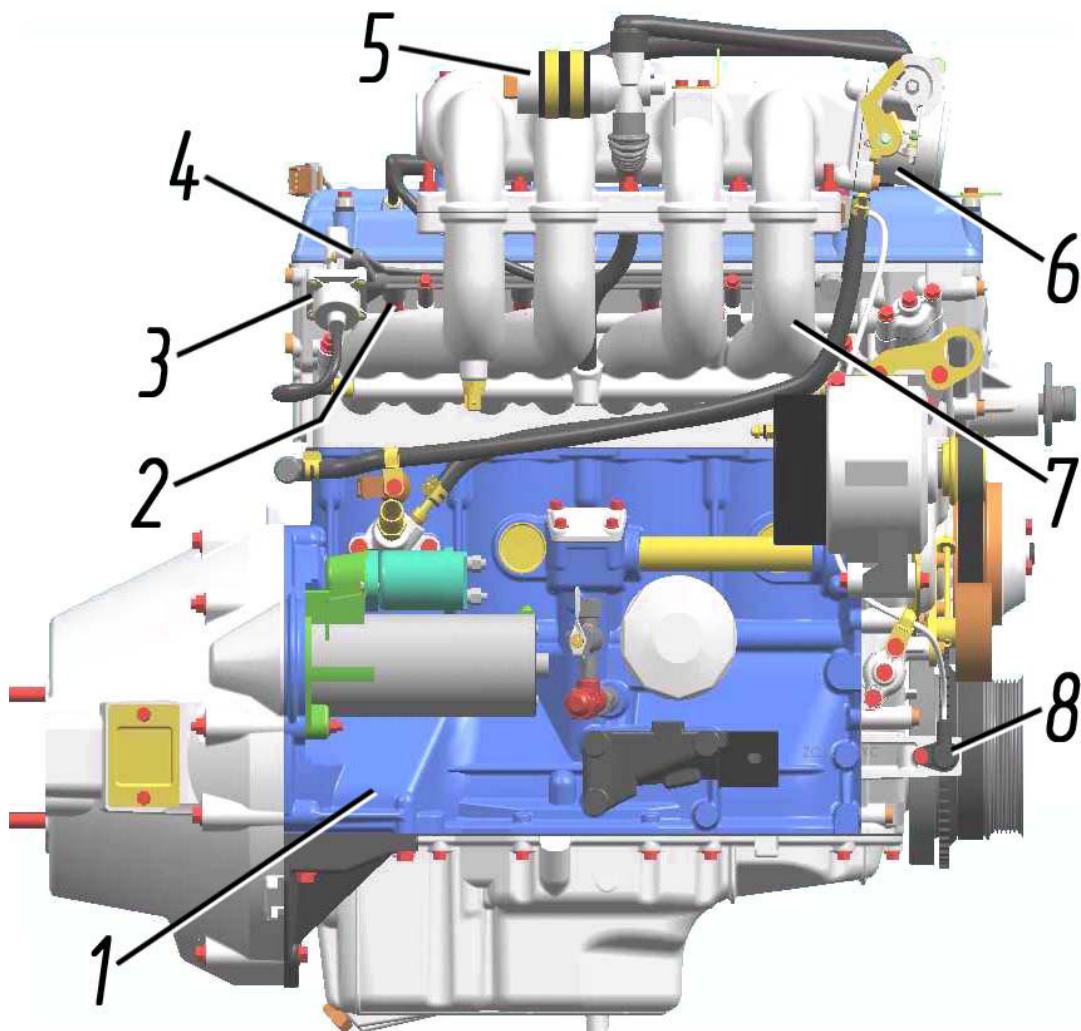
Двигатель ЗМЗ-406 (вид сбоку):
